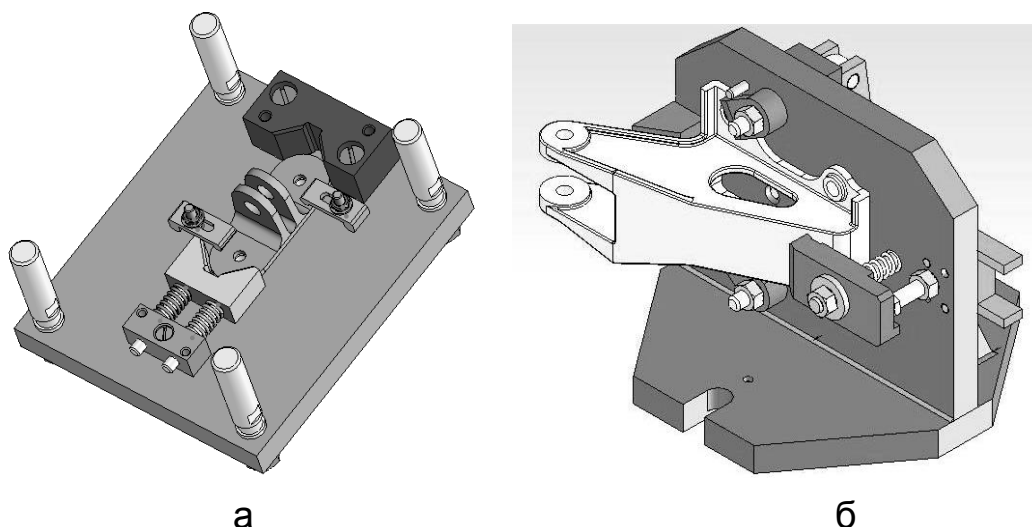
Примеры компоновки корпуса: а – станочного приспособления – кондуктора (вид снизу); б – фрезерного
